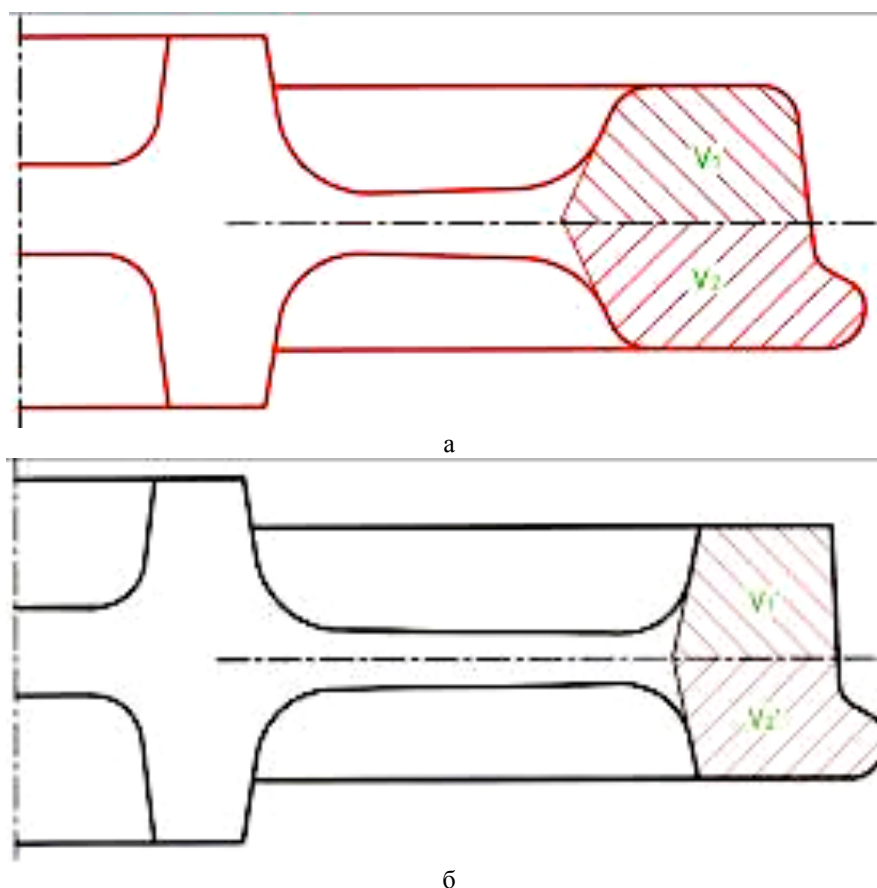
К вопросу обеспечения рациональных потоков металла при прокатке штампованной поковки (а) до требуемых размеров заготовки (б) черного колеса
